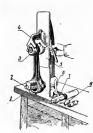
Приспособление для проверки относительного расположения верхней и инжней головок шатуна:
